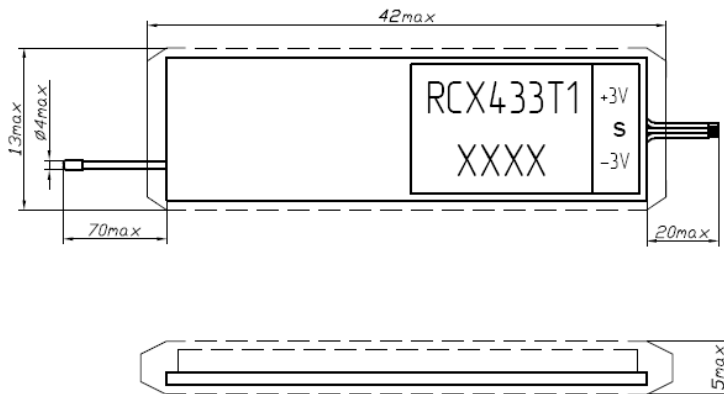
Габаритные размеры передатчика RCX433T1
